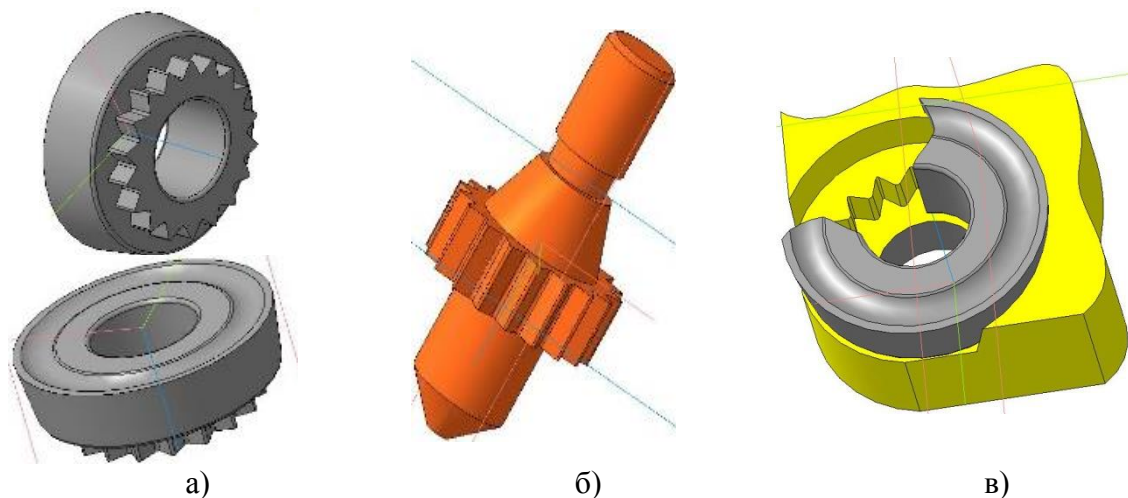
Конструкція круглої пластини а) спеціального електрода для виготовлення посадочного місця б) фрагмент конструкції різального інструменту в)
